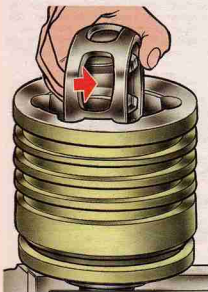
Извлечение сепаратора в сборе с обоймой из корпуса шарнира
